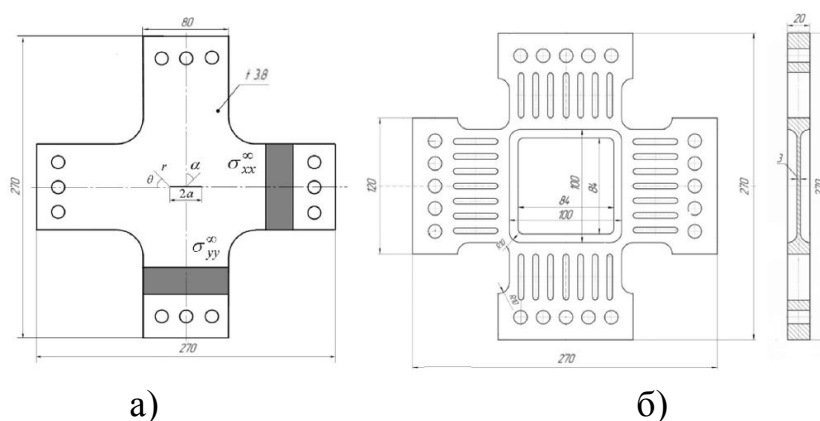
Крестообразные образцы для испытаний при двухосном нагружении
